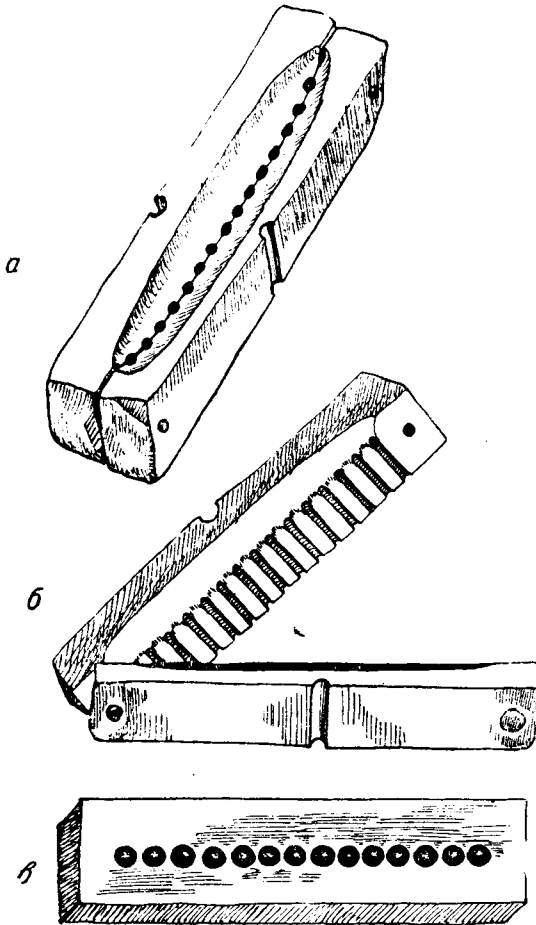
а — общий вид литниковой системы: деревянный разъемный брусочек с общей литниковой чашей и 15-литниковыми канальцами; б — то же в раздвинутом виде; в — металлическая форма в виде пластинки с чашеобразными углублениями, являющимися формочками для отливки выпуклых свинцовых бляшек (см. рис. 2, е)
